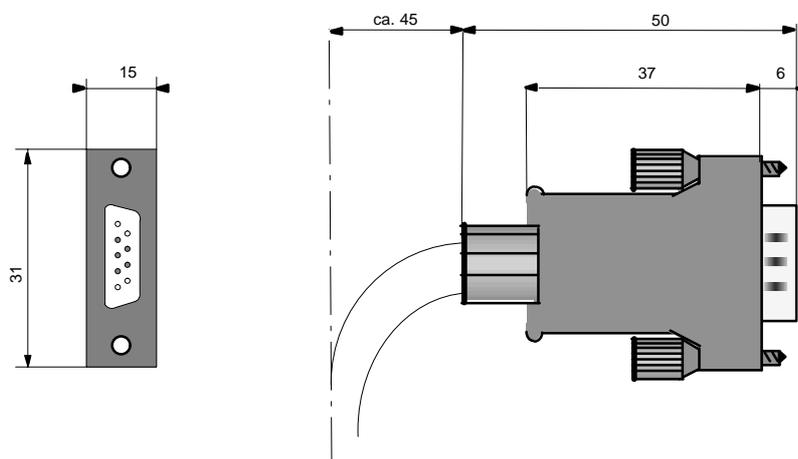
9-poliger Sub-D-Stecker an konfektionierter Leitung (Maße in mm)
